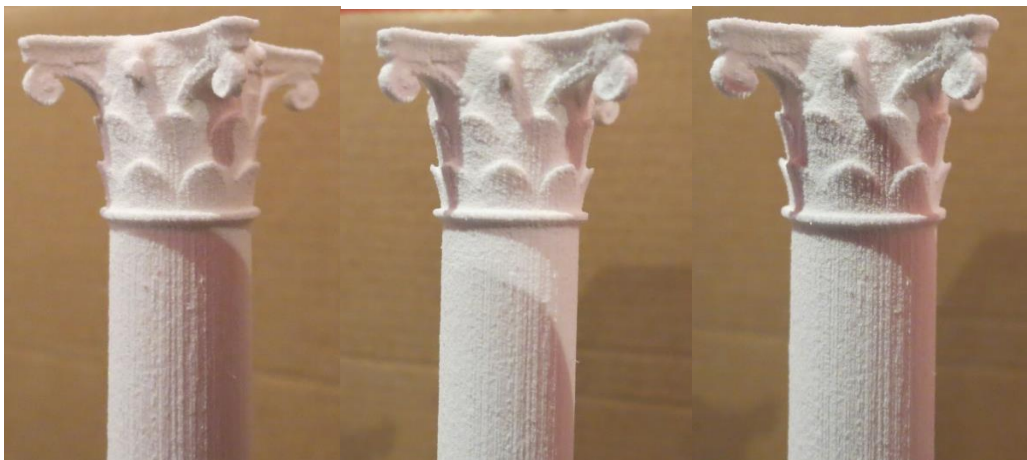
Protótipo de capitel coríntio e fuste fabricado com impressora 3d Zcorp.
